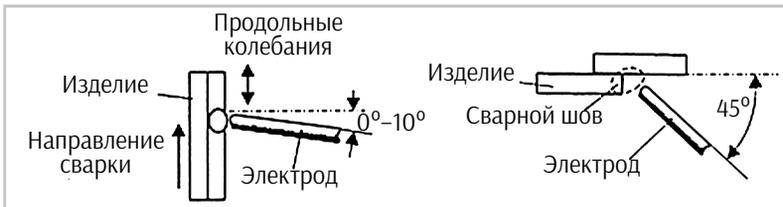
Положение электрода при сварке нахлесточного соединения в вертикальном положении снизу вверх
